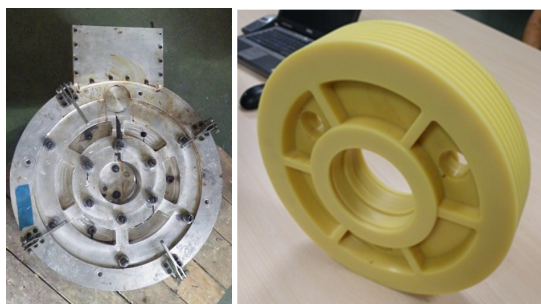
Pieza real fabricada a escala semiindustrial y molde en el que se ha realizado.
